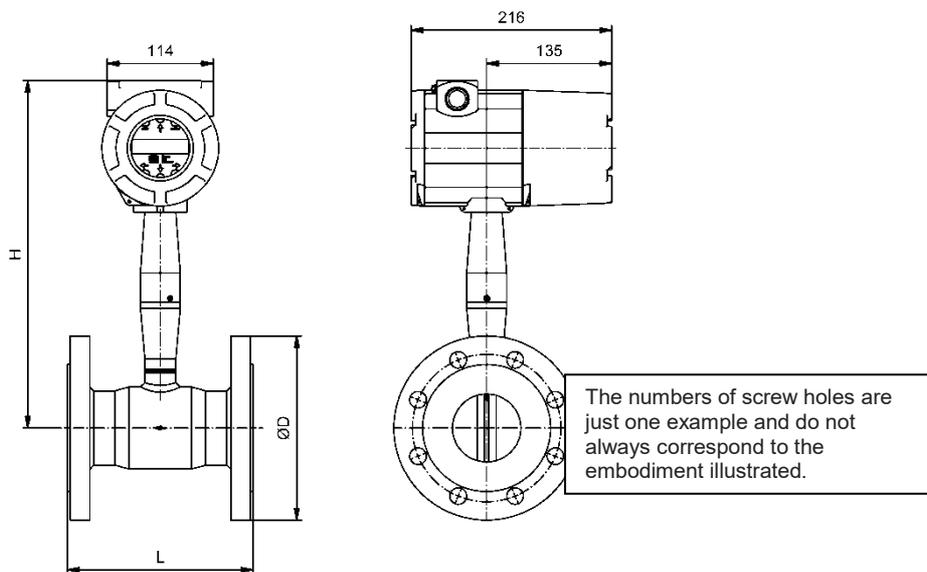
Dimensionen Flanschversion mit aufgebauter Elektronik
